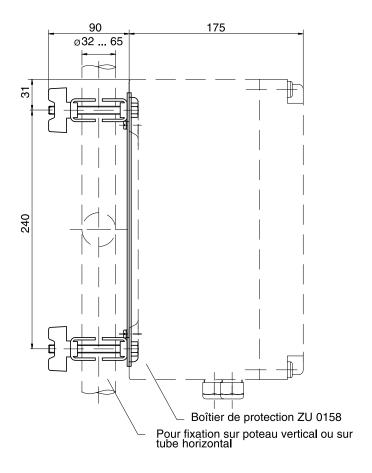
Jeu de colliers pour fixation sur mât ZU 0220 pour boîtier de protection ZU 0158
